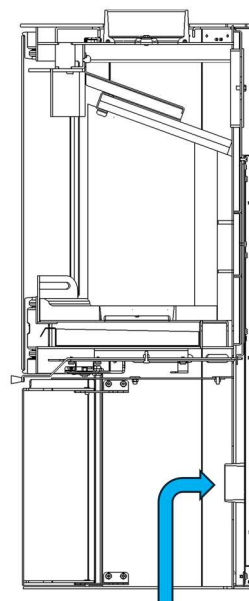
OPZIONE 3 Presa d'aria esterna, utilizzando i set di collegamento
